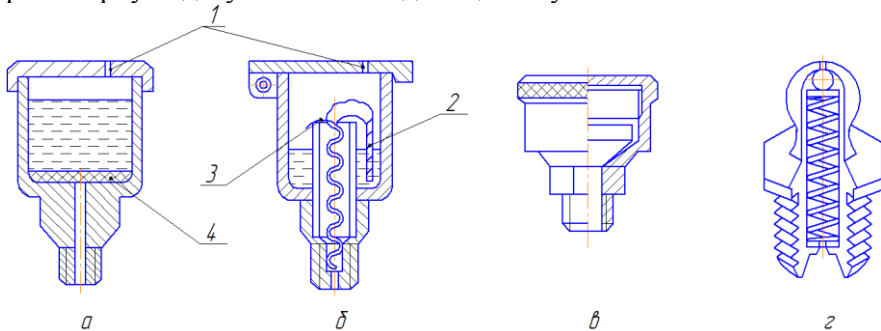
Масельнички: а – резервуарна; б – гнотова (1 – отвір для повітря; 2 – гніт; 3 – вусики; 4 – набивка); в – ковпачкова; г – кулькова пресова
